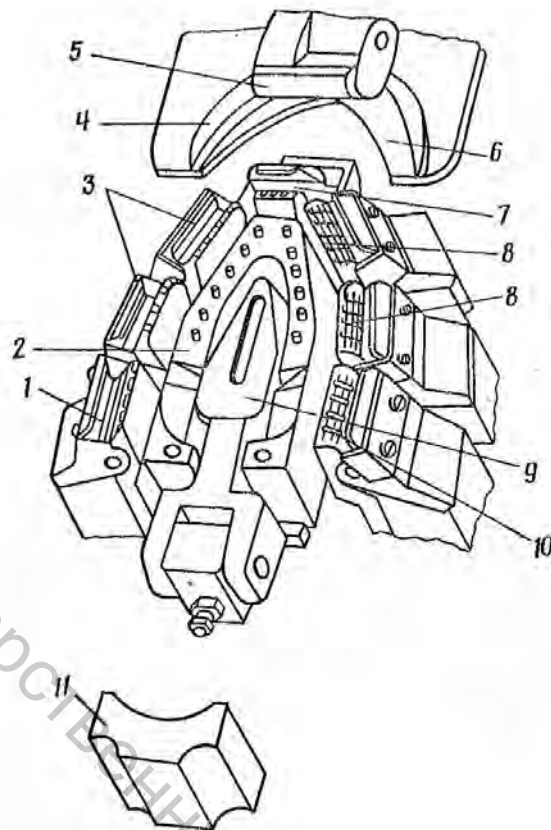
Рабочие органы машины для формования носочно-пучковой части заготовки верха обуви:
